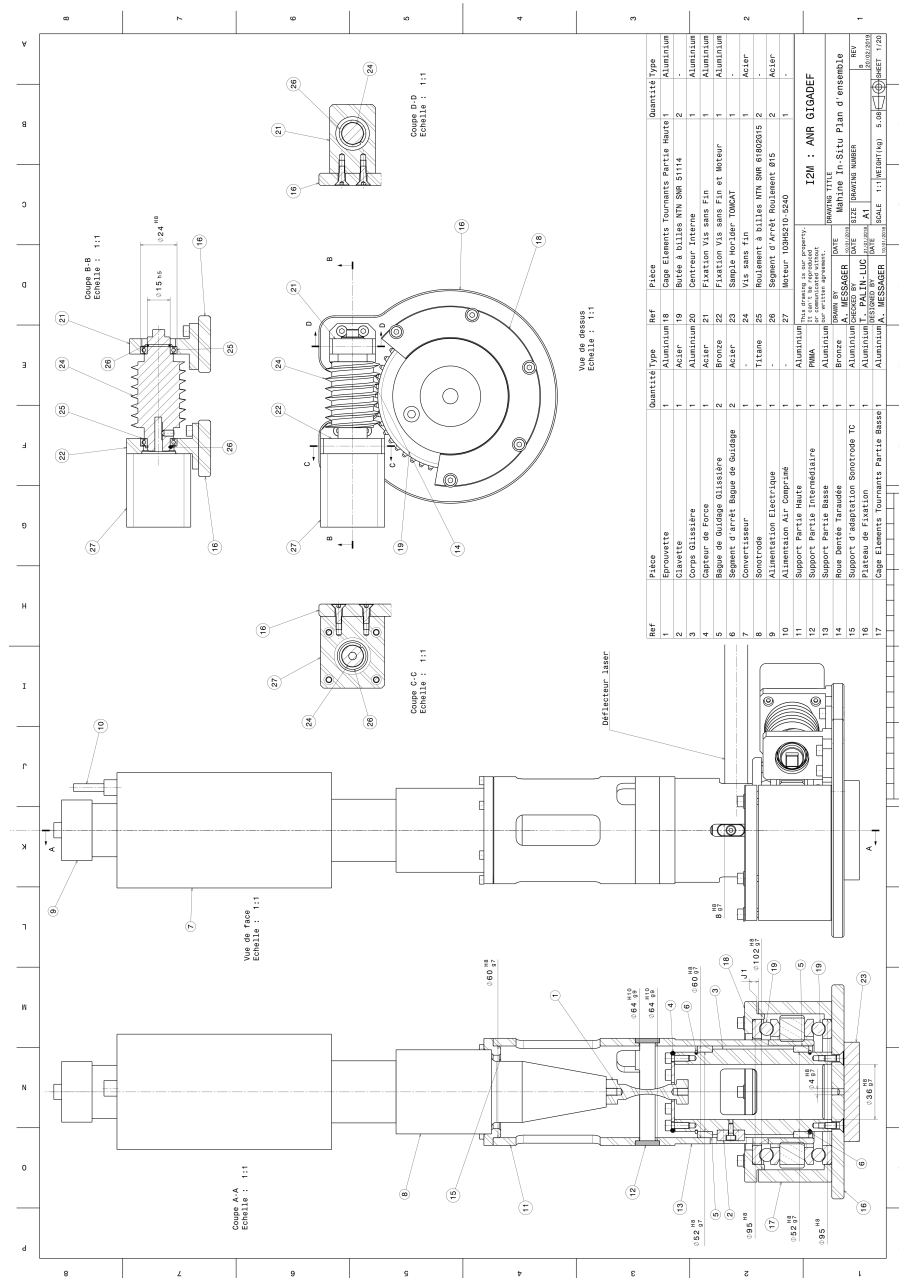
Dessin d'ensemble de la machine d'essai de fatigue ultrasonique in-situ synchrotron.
